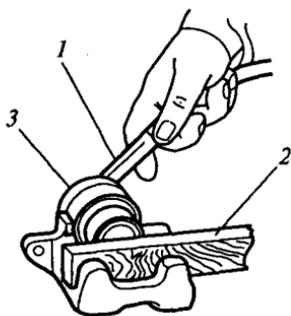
Выталкивание поршня из цилиндра: 1 — шланг с сжатым воздухом; 2 — деревянная прокладка; 3 — цилиндр
